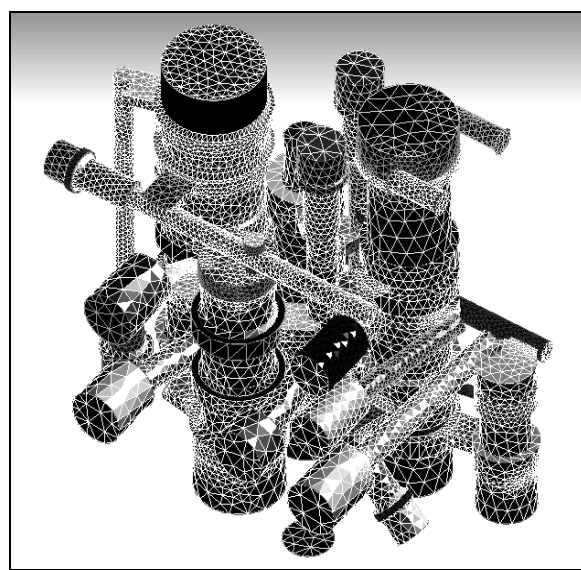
Твёрдотельная модель корпуса агрегата двигателя ЛА
